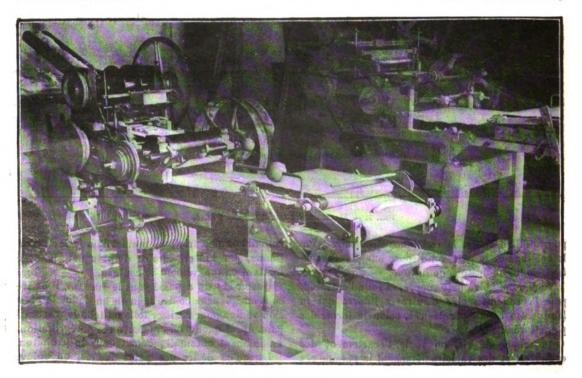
MACHINE A FAIRE LES CROISSANTS.
